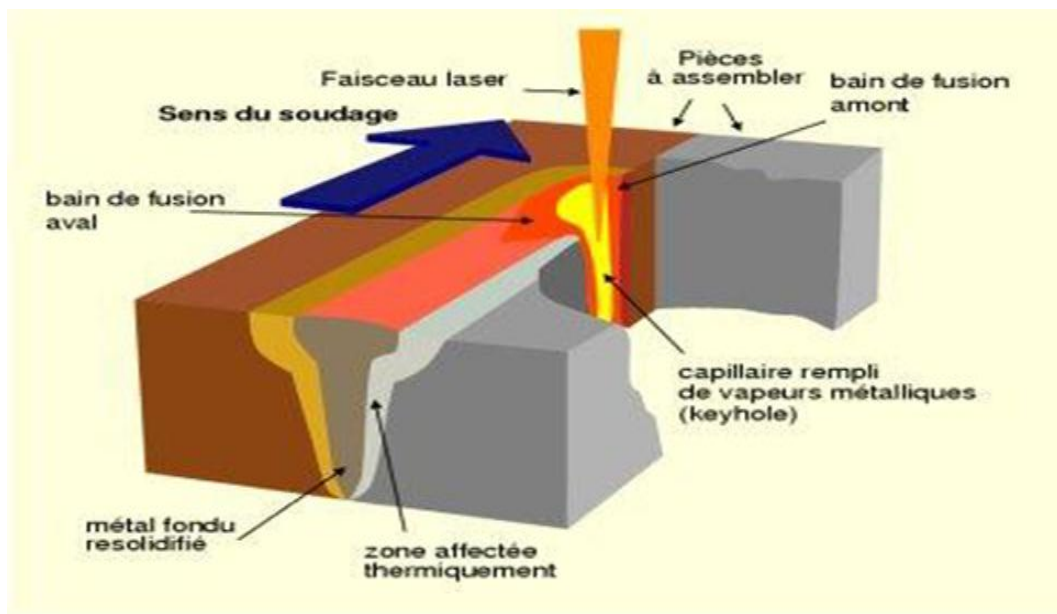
Soudage par faisceau Laser [24].
